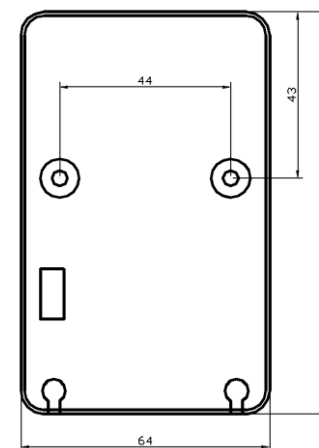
Габаритные и установочные размеры ИПР-55
